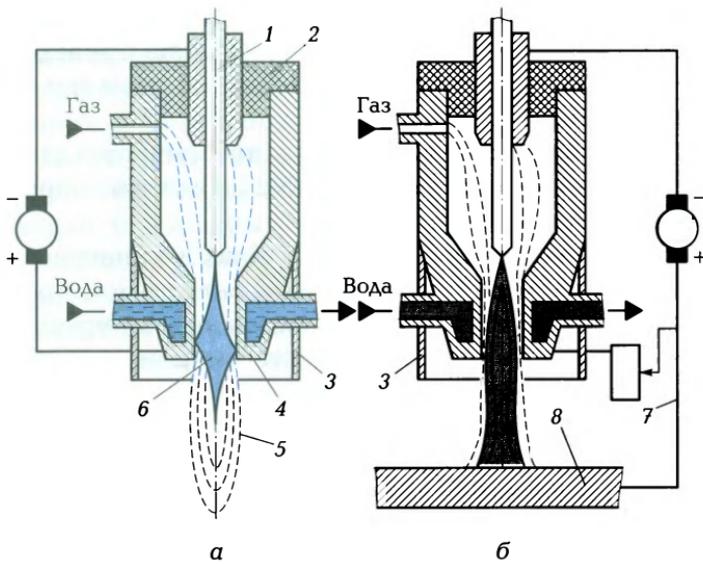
Схемы сварочных дуговых плазменных головок:
